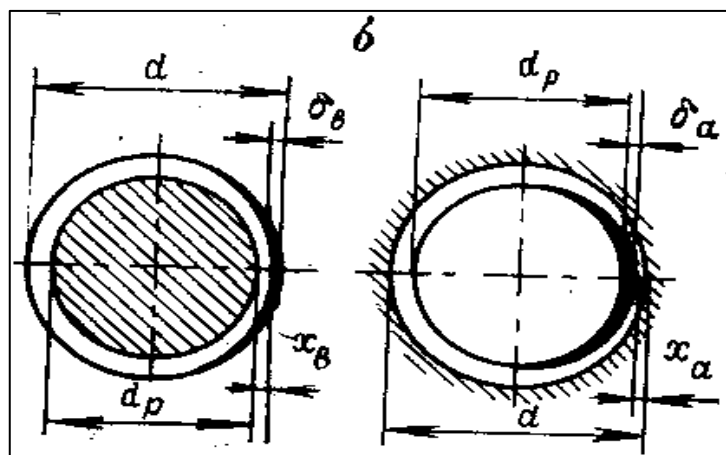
Схема обработки деталей под ремонтный размер: в — для вала; б — для отверстия
